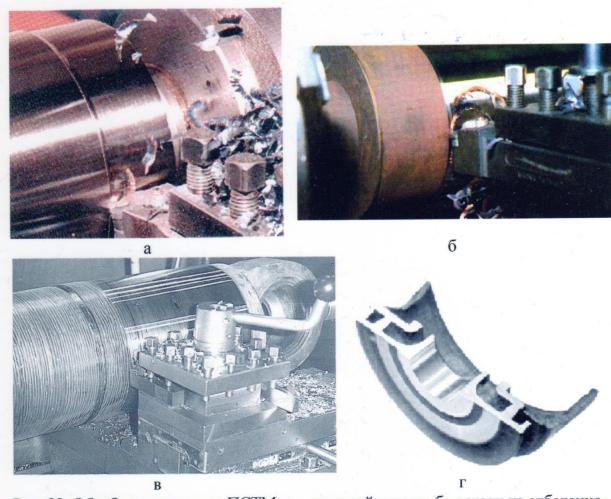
Обработка резцом из ПСТМ: а – стальной детали; б –детали.из отбеленного чугуна; в – наплавленной детали; г – обработанная напыленная деталь.
